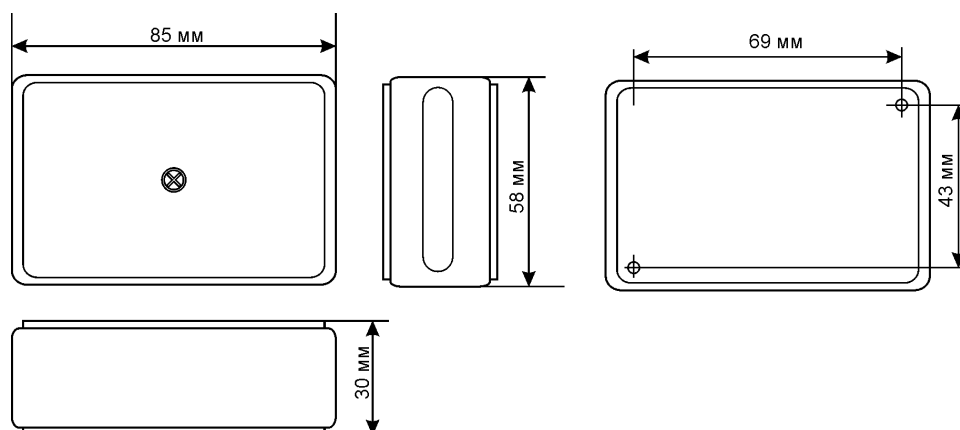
Габаритные и установочные размеры «СФ-БЗЛ».
